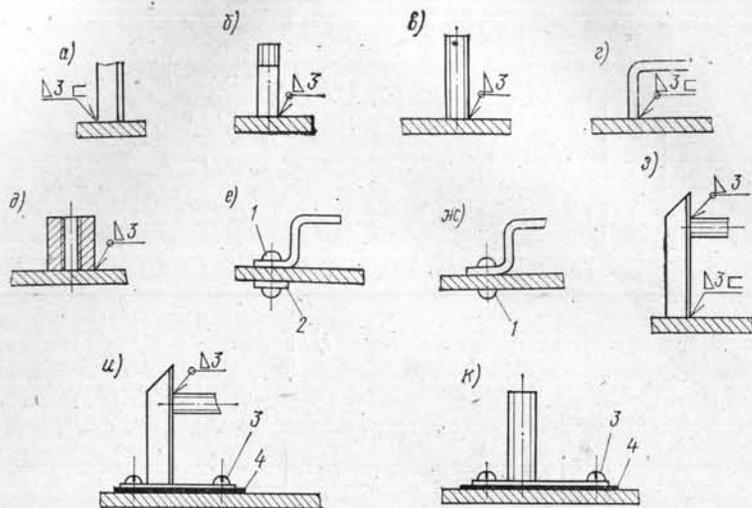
Детали для установки электроустановочных конструкций на металлических основаниях: а — стойка; б — шпилька; в — труба приварная; г — мост приварной; д — бонка; е — мост приклепываемый стальной оцинкованный с прокладкой; ж — мост приклепываемый стальной оцинкованный; з — консоль приварная; и — консоль, закрепляемая винтами; к — труба, закрепляемая винтами.
